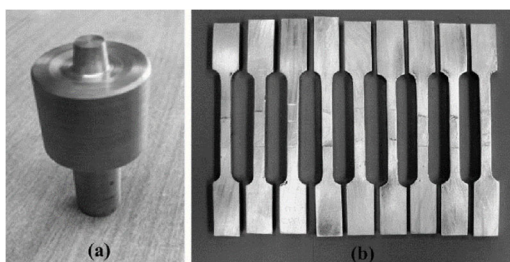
(a) Herramienta de soldadura por fricción (b) Probetas para ensayo de tracción soldadas con el proceso FSW (Elaboración propia).
